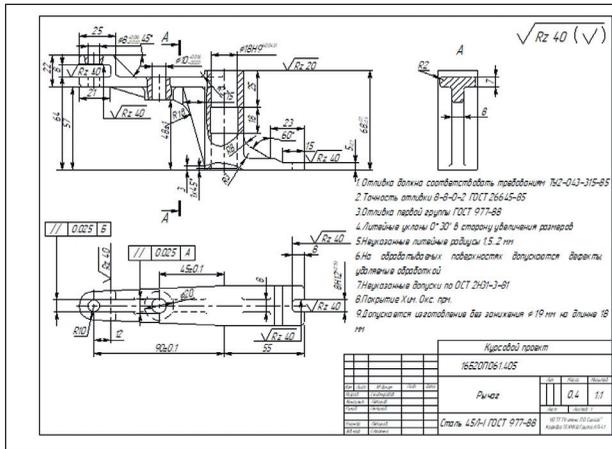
Параметризованный чертеж детали «рычаг 16Б20П.061.405»
